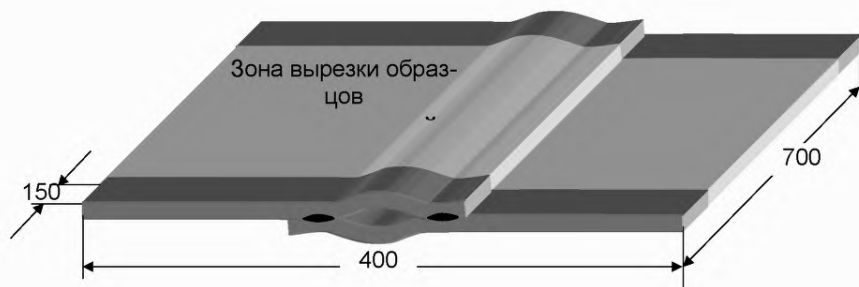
Контрольное сварное соединение типа Н.
